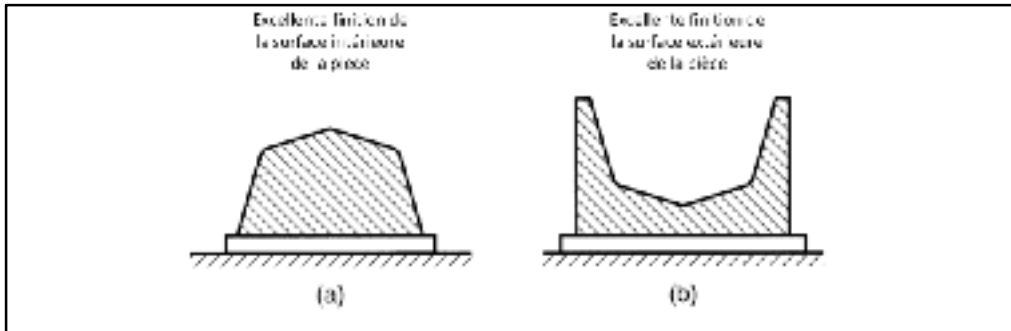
Types de moules ouverts; (a) Moule mâle; (b) Moule femelle
